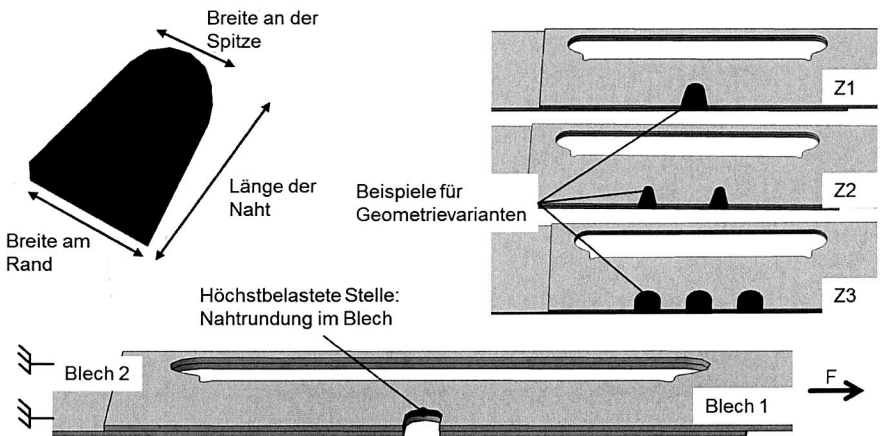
Parametrisierung der Schweißnaht.
